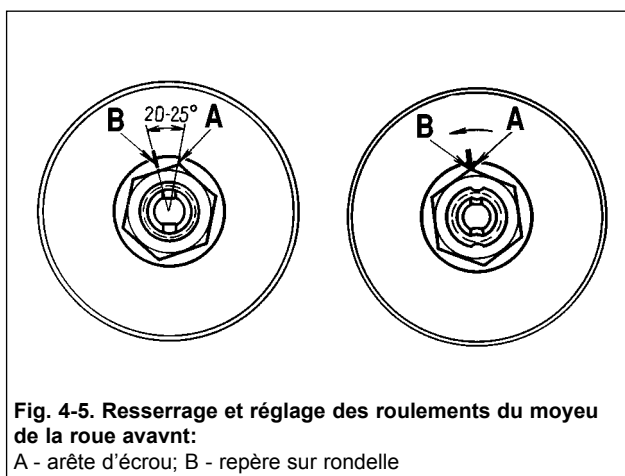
Resserrage et réglage des roulements du moyeu de la roue avant: A - arête d'écrou; B - repère sur rondelle
